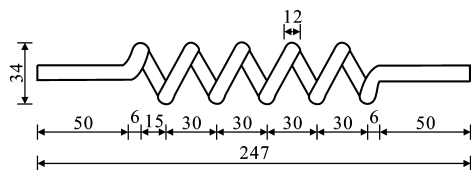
SMA 螺旋弹簧尺寸 (单位: mm)
